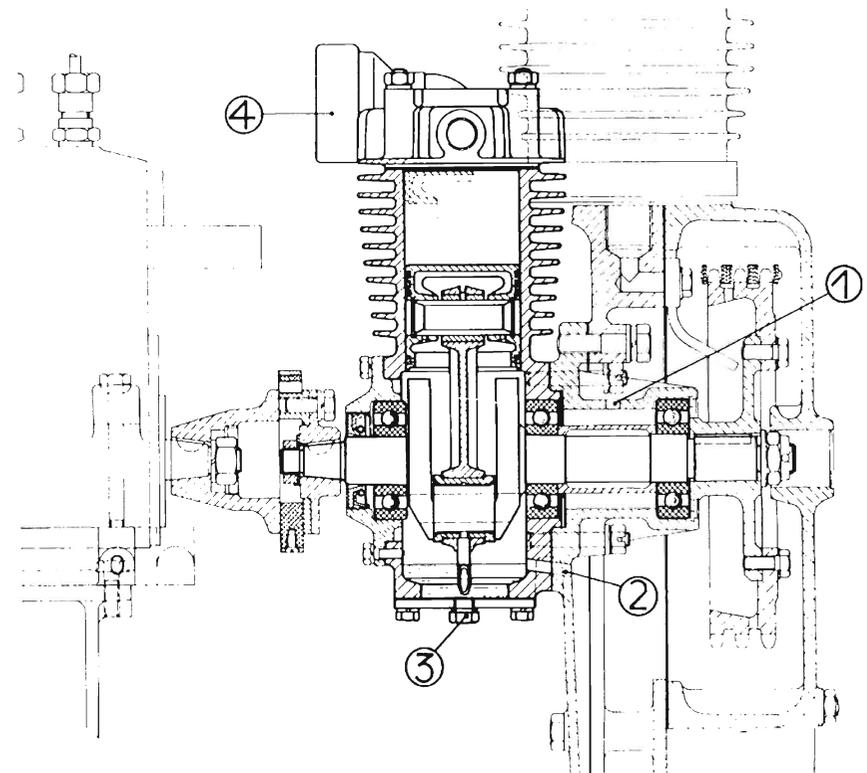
Längsschnitt durch den Einzyylinder-Kompressor
